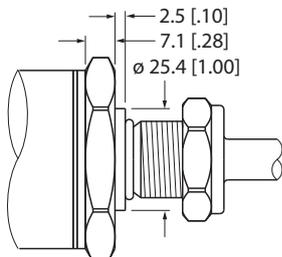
Ausführung mit Raised Face (R10) – Gehäusemutter mit Gewinde
